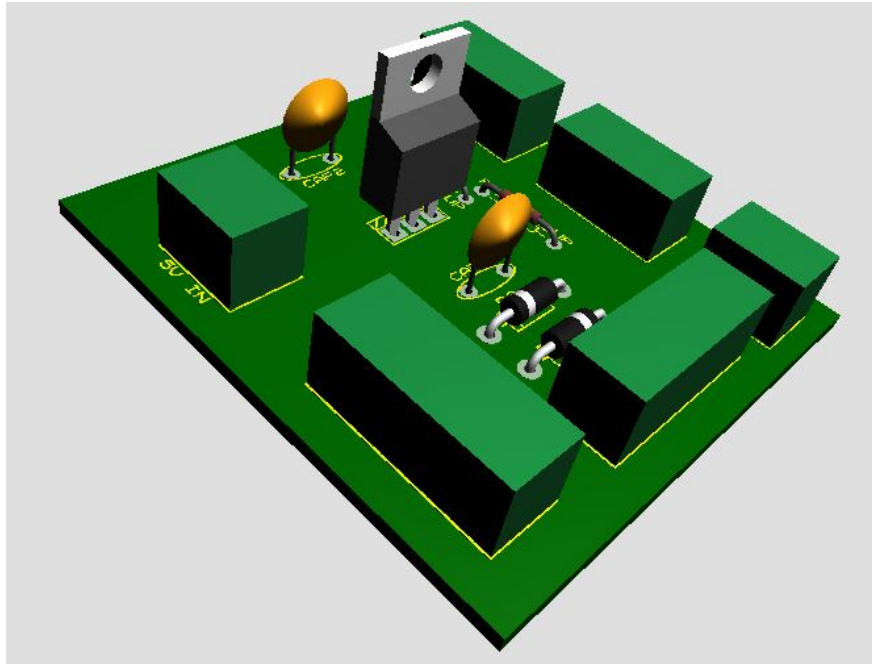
Esquema PCB del circuito impreso diseñado. Esquema elaborado por el autor.
